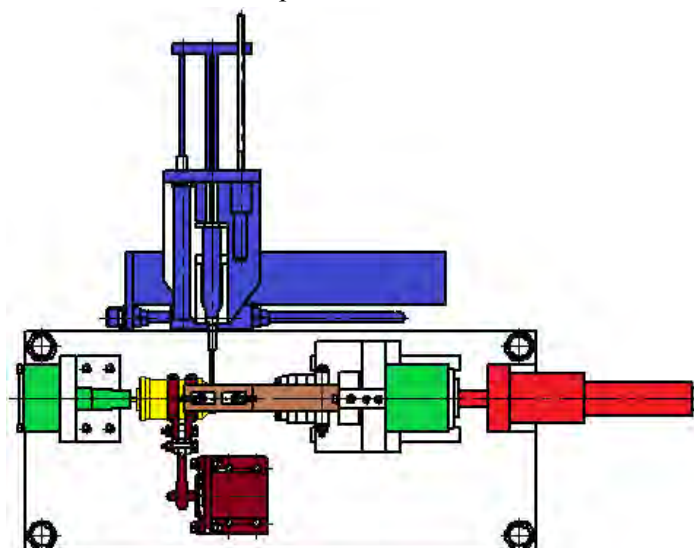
Установка для пайки якорей двигателей постоянного тока
